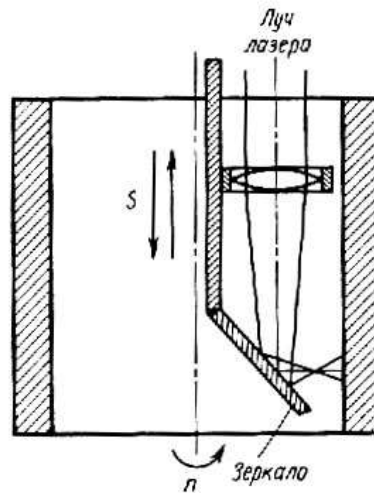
Схема упрочнения внутренней цилиндрической поверхности
